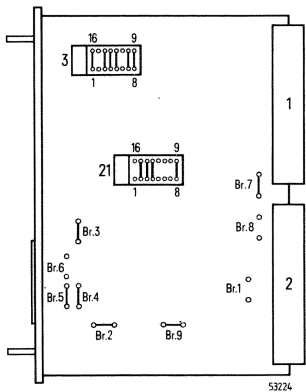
Zentralbaugruppe 6ES5 925-3, Einbaulage der Brücken
